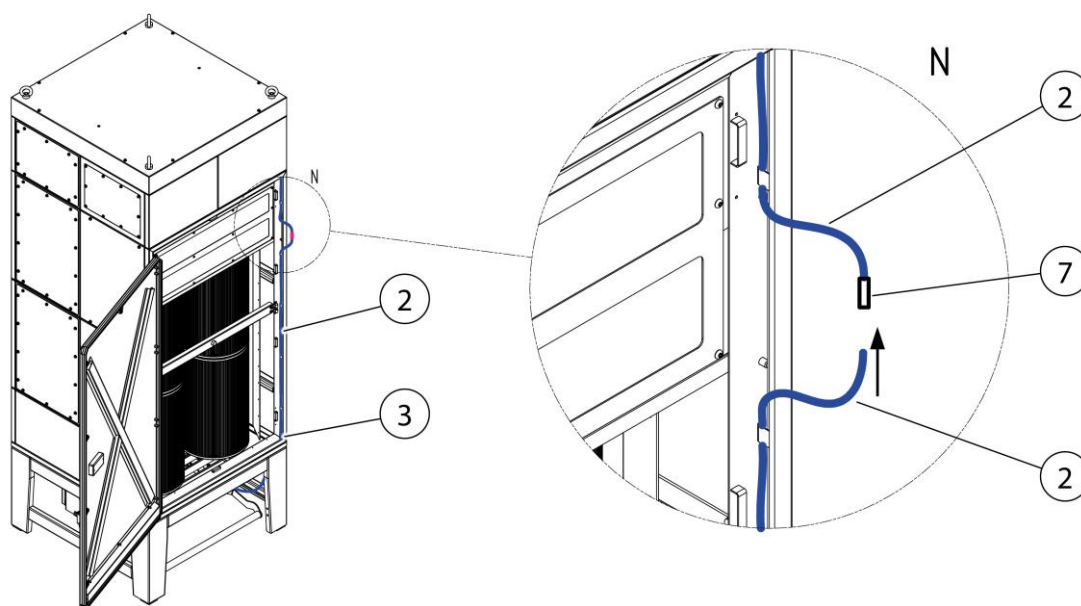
Montaje - Tendido de la manguera de aire comprimido
